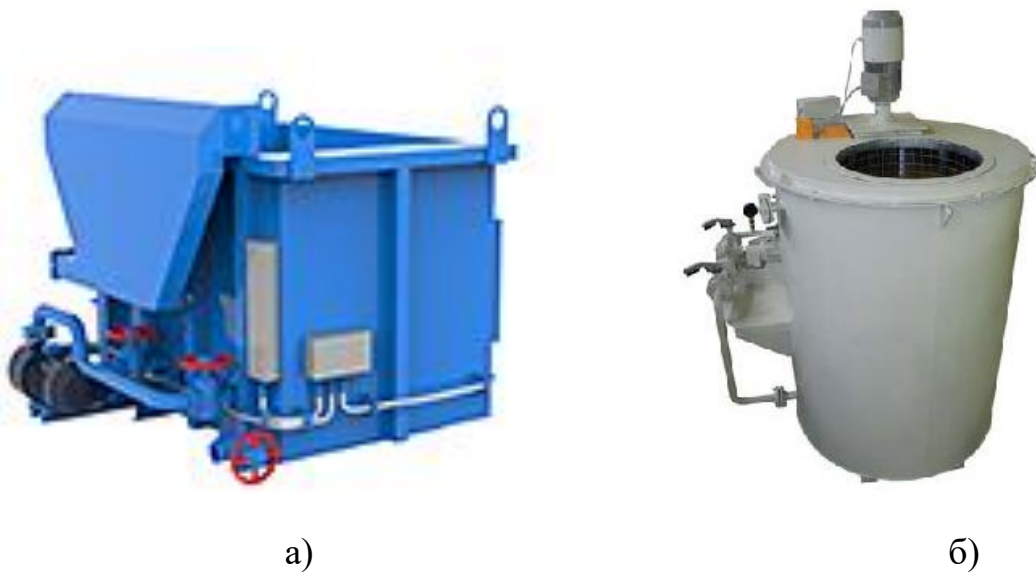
Баки для гартування: а) прямокутний бак; б) циліндричний
